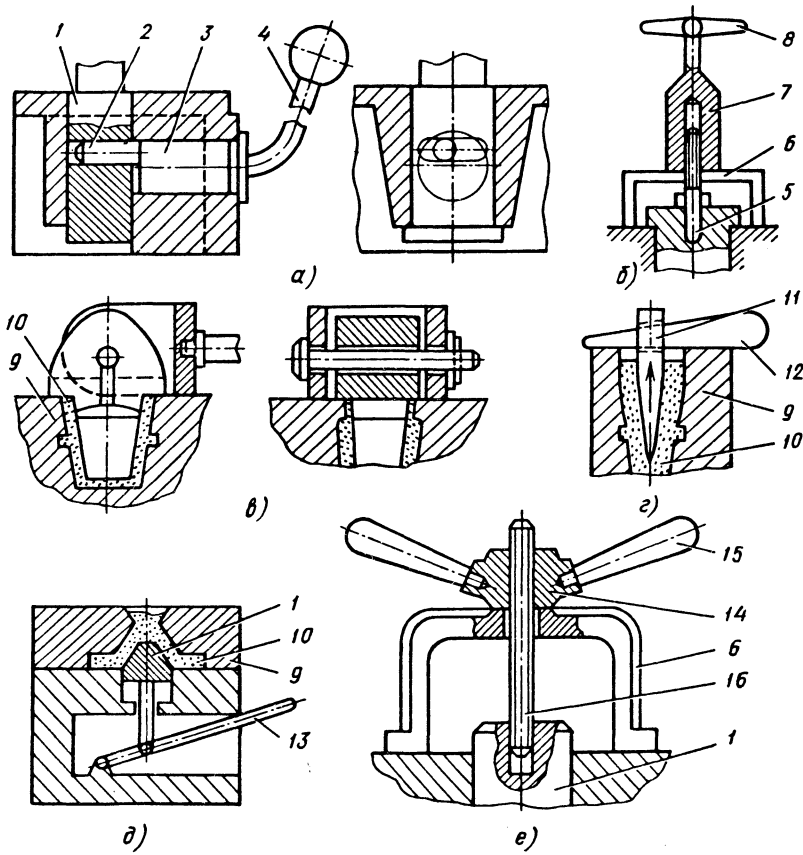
Ручные приспособления и механизмы для извлечения металлических стержней:
